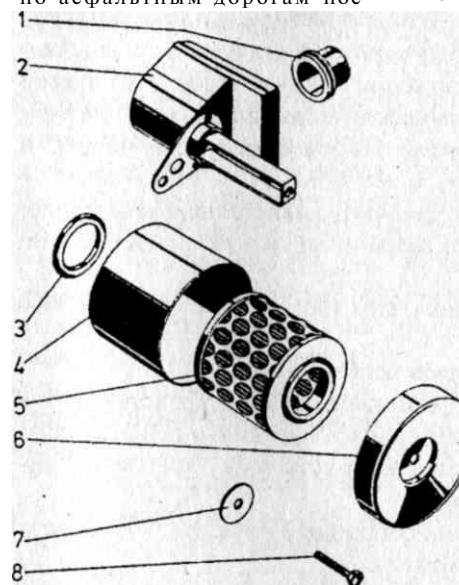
Воздушный фильтр мокика "Карпаты": 1 - втулка; 2 - ресивер; 3 - кольцо; 4 - банка; 5 - элемент фильтрующий; 6 - крышка; 7 - шайба упорная; 8 - болт
